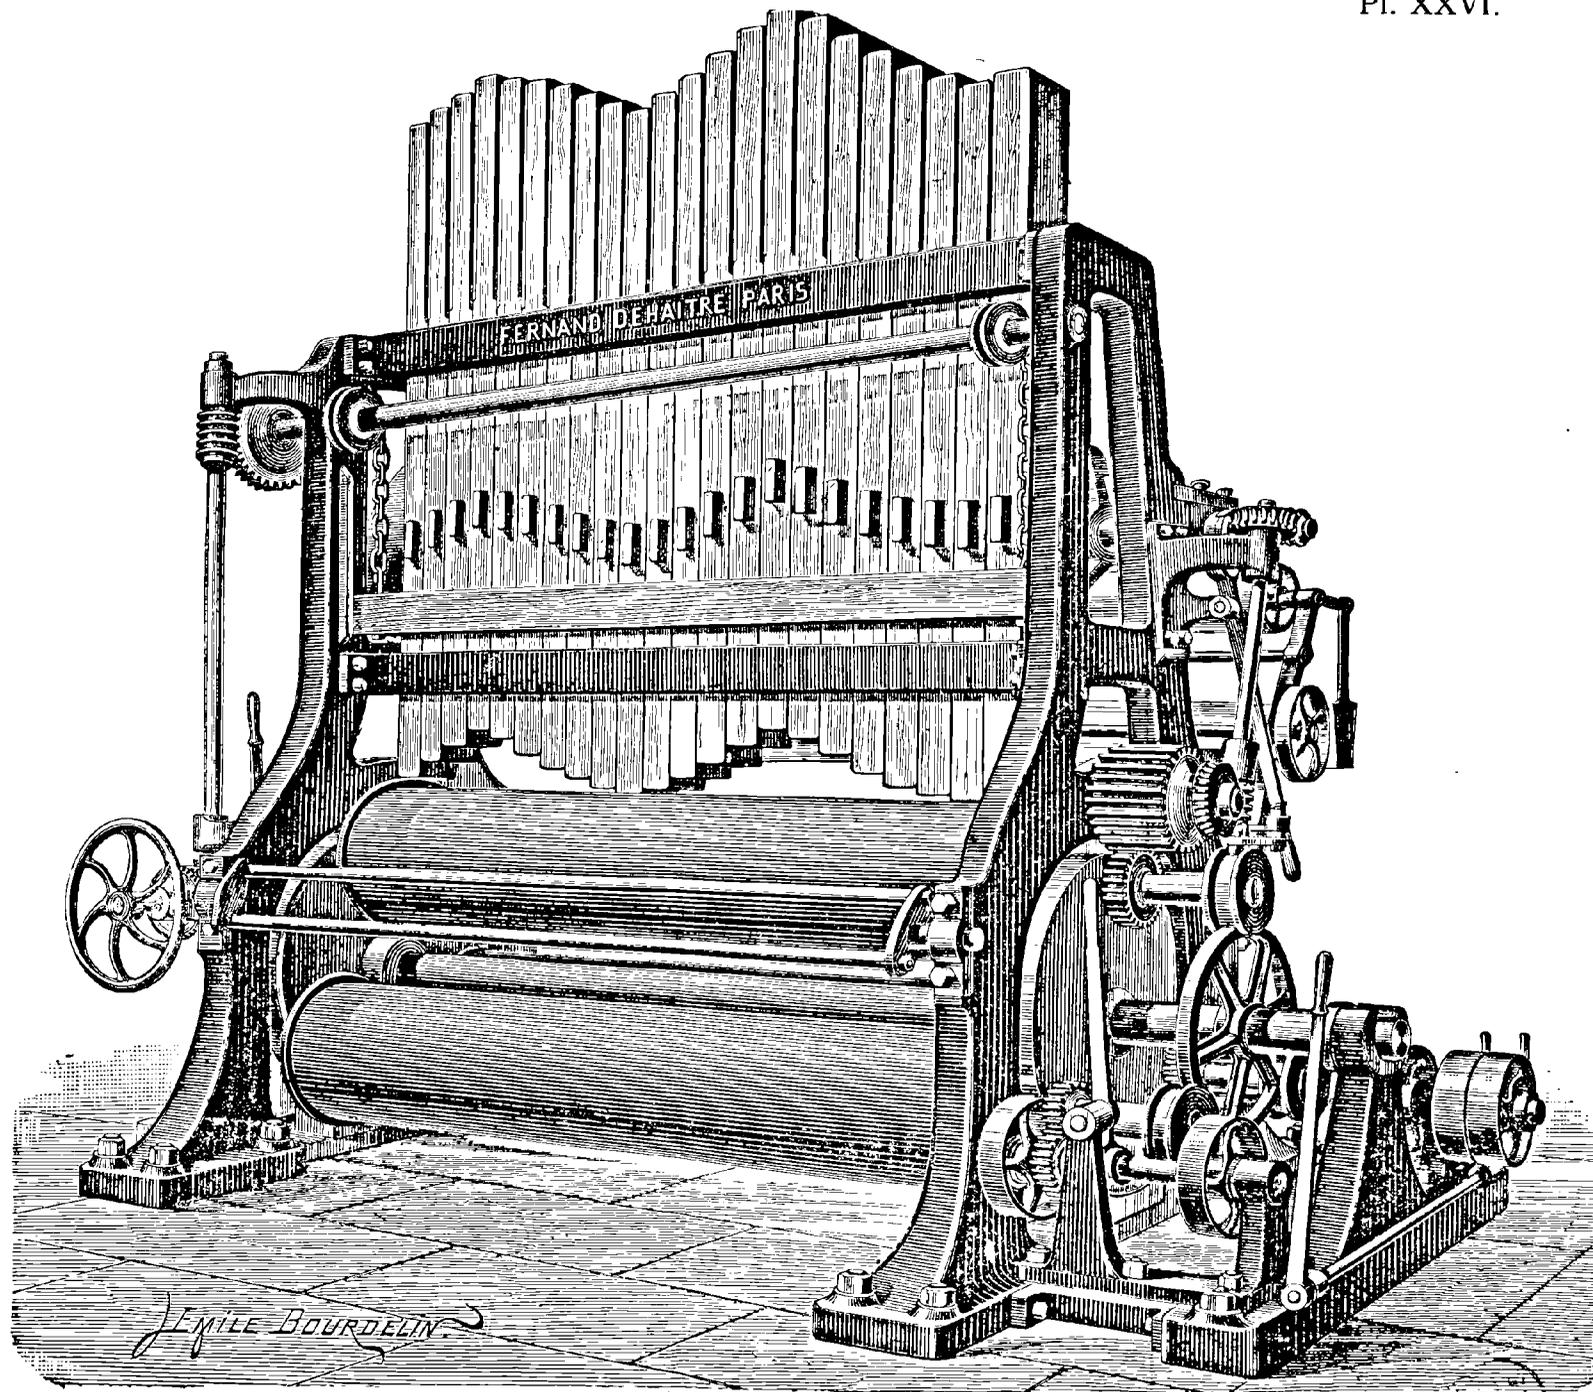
Manteuseuse ou Bœtte. — Vue de derrière.
